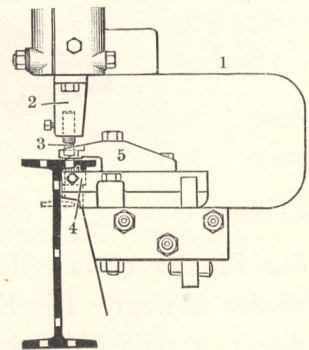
Universalwerkzeuge zur Lochmaschine.
